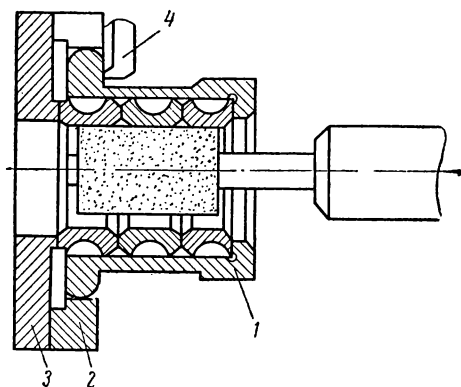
Приспособление для шлифования отверстий трех колец за один установ
